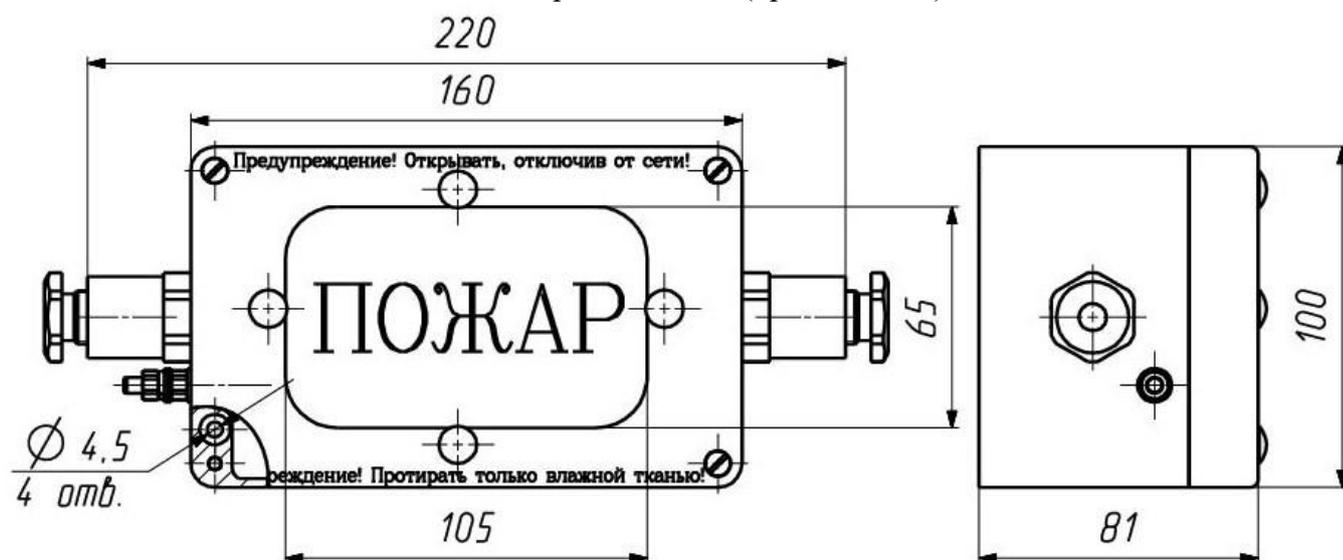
Общий вид с элементами обеспечения взрывозащиты, габаритные, присоединительные размеры табло светового модели ExTC-2.
